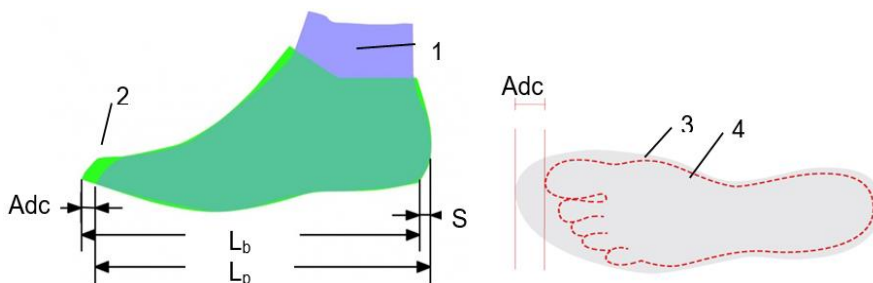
Poziția piciorului în raport cu calapodul, unde Adc – adaosul decorativ-constructiv; Lb – lungimea brânțului; Lp – lungimea piciorului; S – amplitudinea curburii posterioare a calapodului; 1 – picior; 2 – calapod; 3 – conturul brânțului; 4 – conturul de gabarit al piciorului
